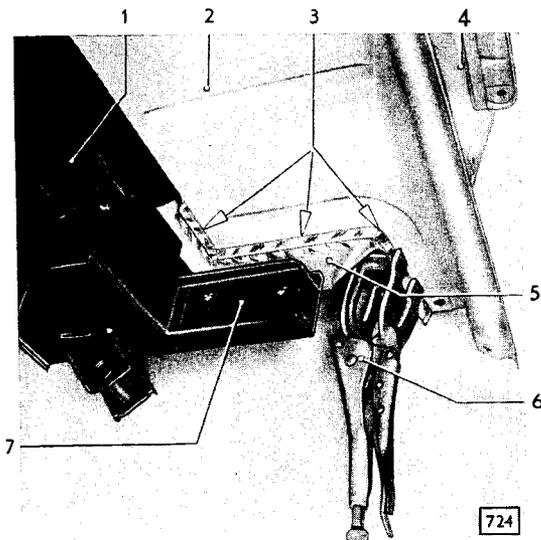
Unteres Luftleitblech in Einbaulage gebracht und festgespannt
